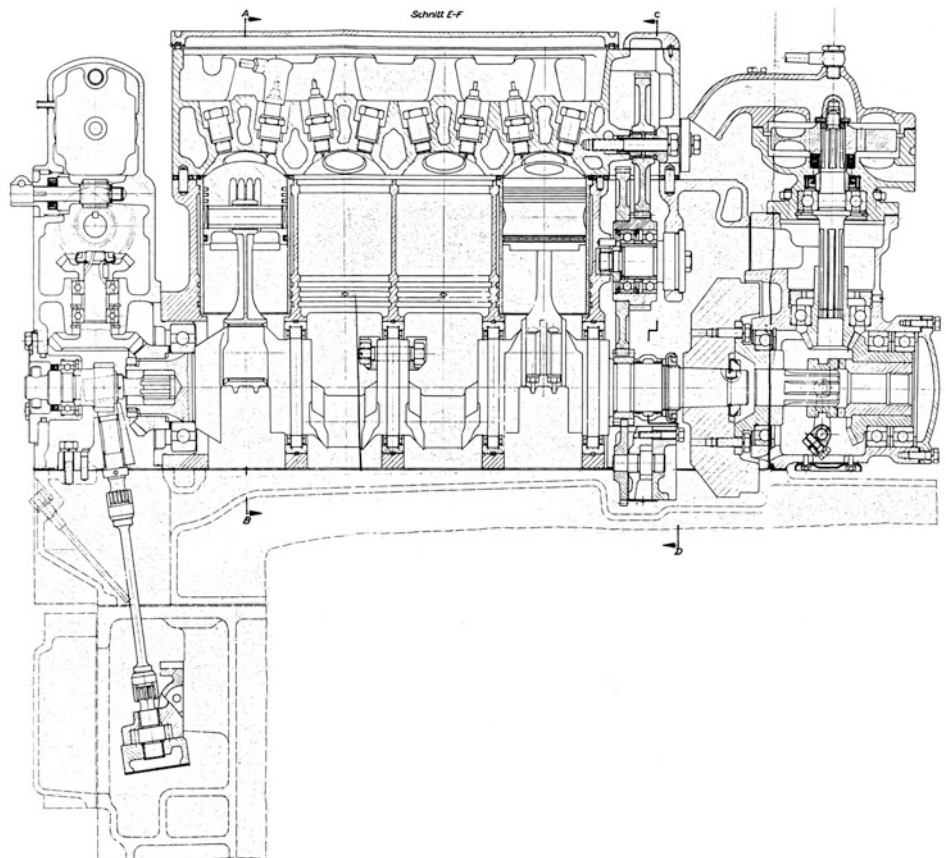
Querschnitt des Hilfsmotors HL 11. Der Motor hat einen gemeinsamen Kühlwasserkreis mit dem Hauptmotor HL 295, um diesen vorzuwärmen bzw. warm zu halten. In diesem Querschnitt sieht man die groß dimensionierten Kühlwasserkanäle des HL 11 mit den Übertritten zum Kühlkreis des Hauptmotors. Die beiden »Hörner« seitlich sind die an das HL-11-Kurbelgehäuse angegossenen Luftansaugstutzen des HL-295-Hauptmotors
